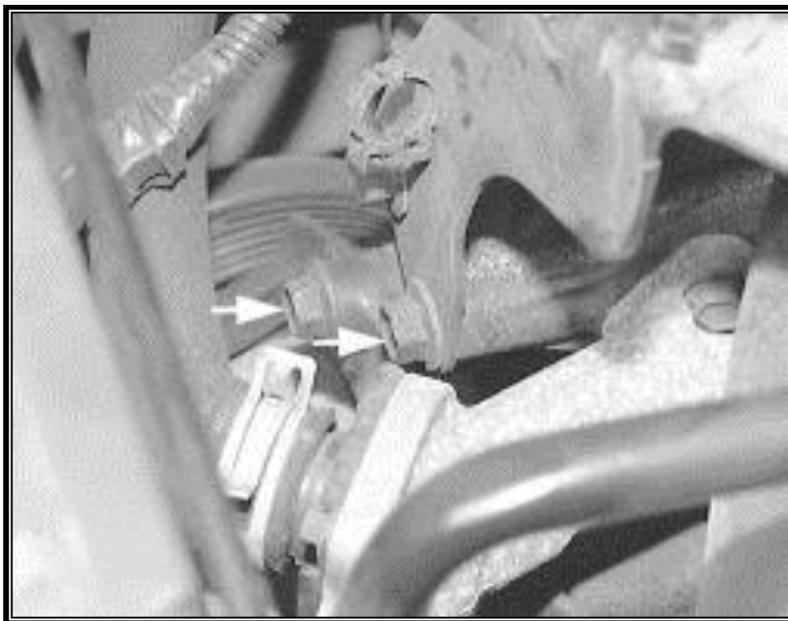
Soporte inferior del alternador. (AutoZone, 2018)
